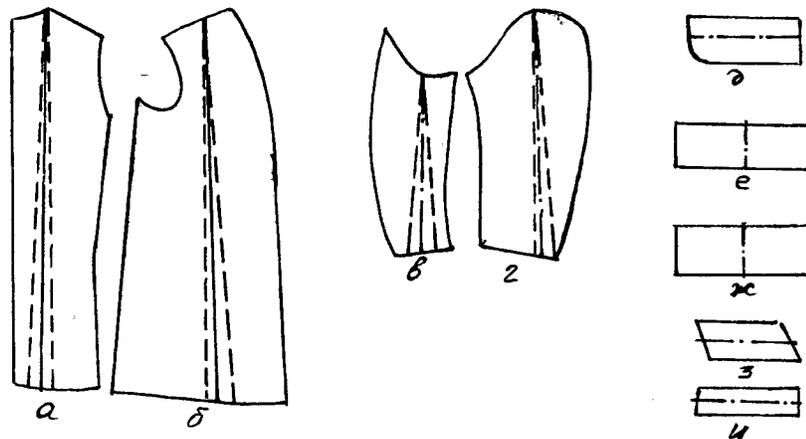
Детали подкладки пиджака: а – спинка; б – полочка; в – нижняя часть рукава; г – верхняя часть рукава; д – подкладка клапана; е – подзор бокового кармана; ж – подзор внутреннего кармана; з – подкладка листочки; и – вешалка.
